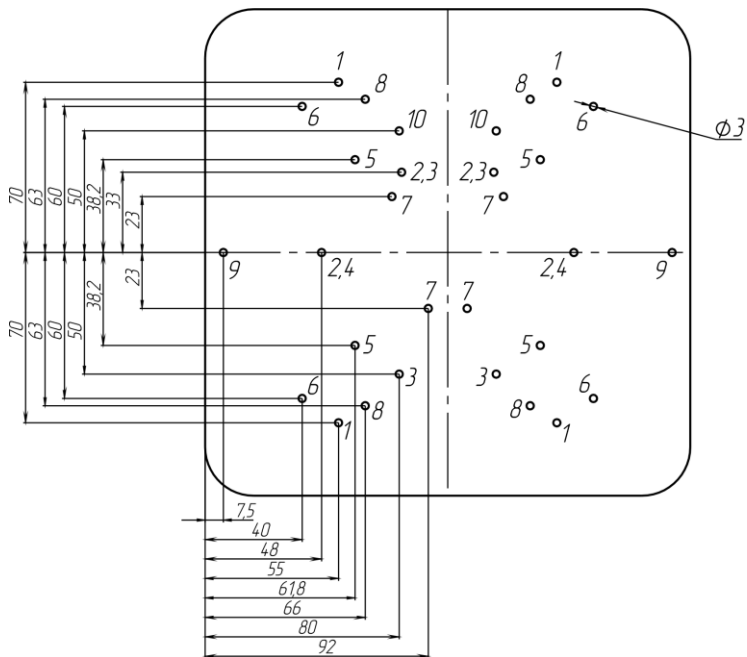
Габаритные размеры и разметка площадки универсальной (1) под оборудование
